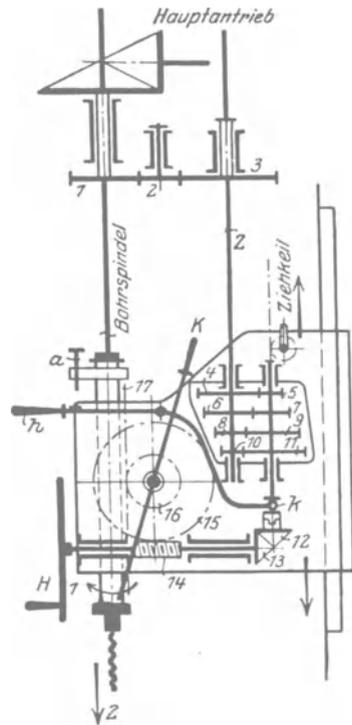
Selbsttätige Steuerung der Bohrspindel.
